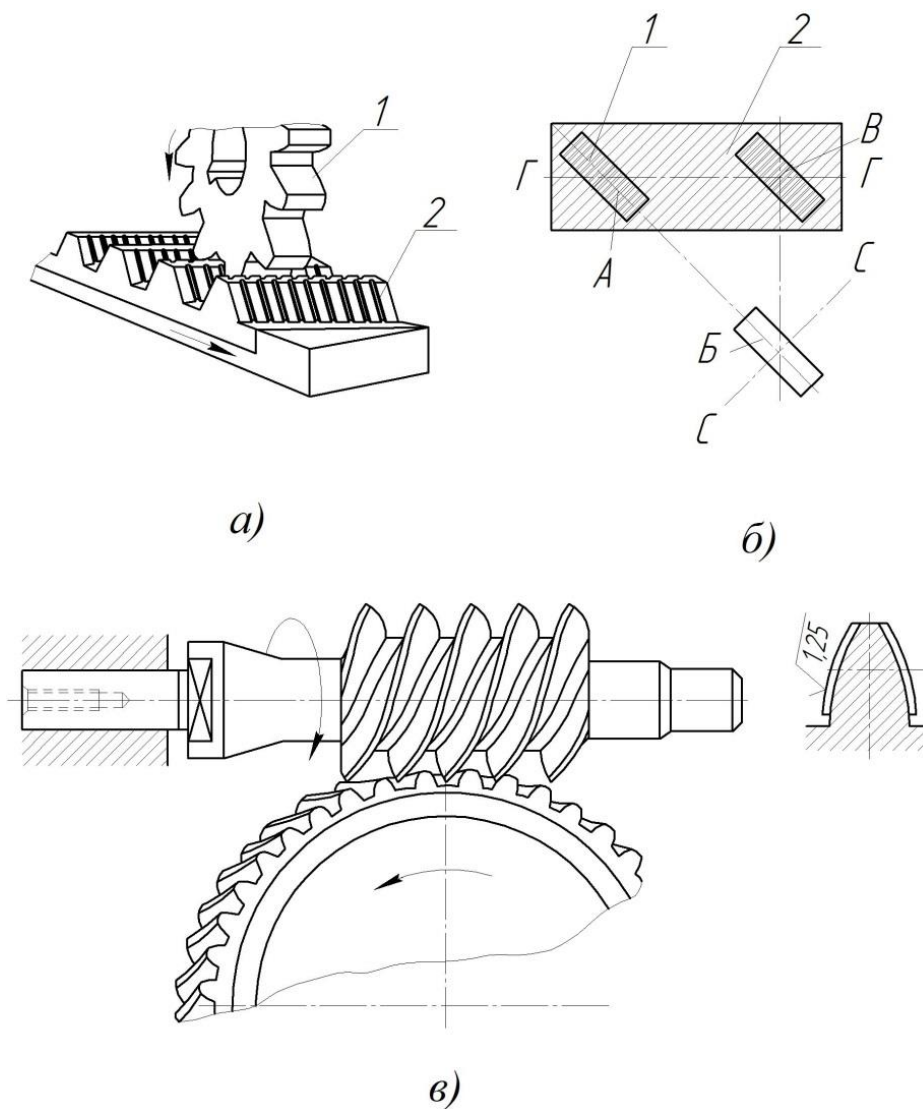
Шевінгування шевер-рейкою і шевер-черв'яком:
